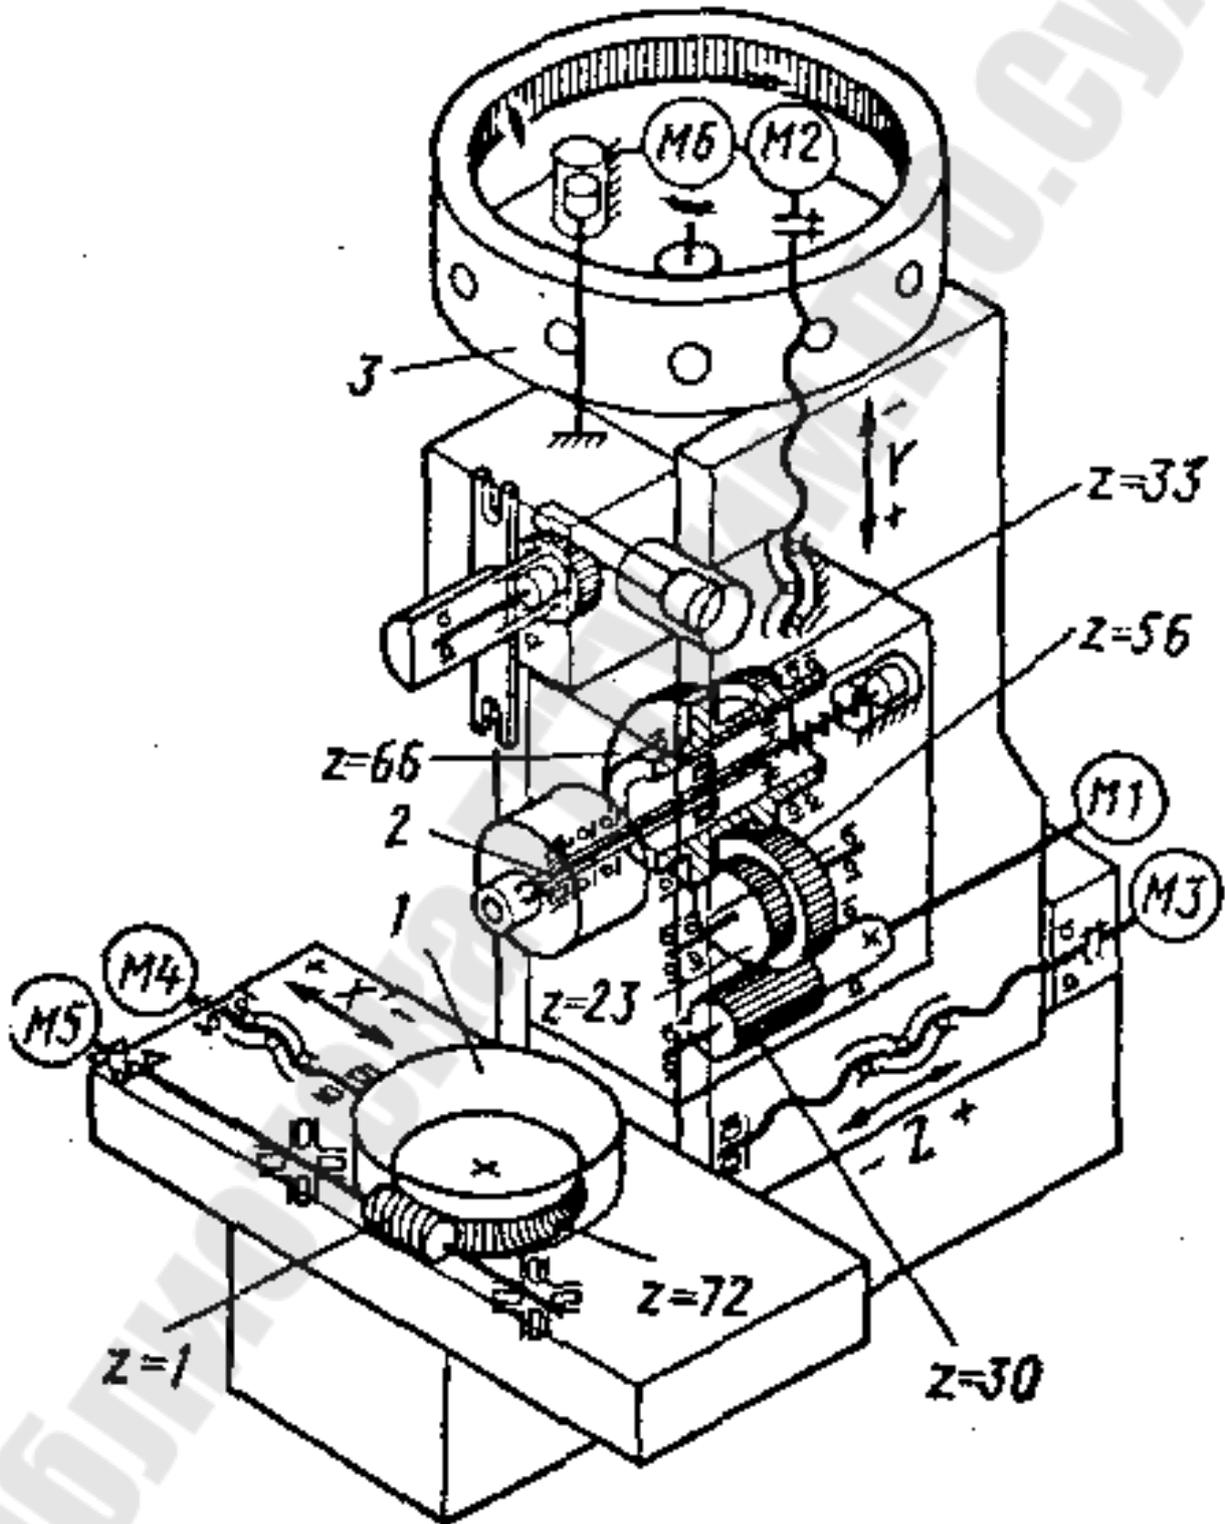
Кинематическая схема многоцелевого станка
